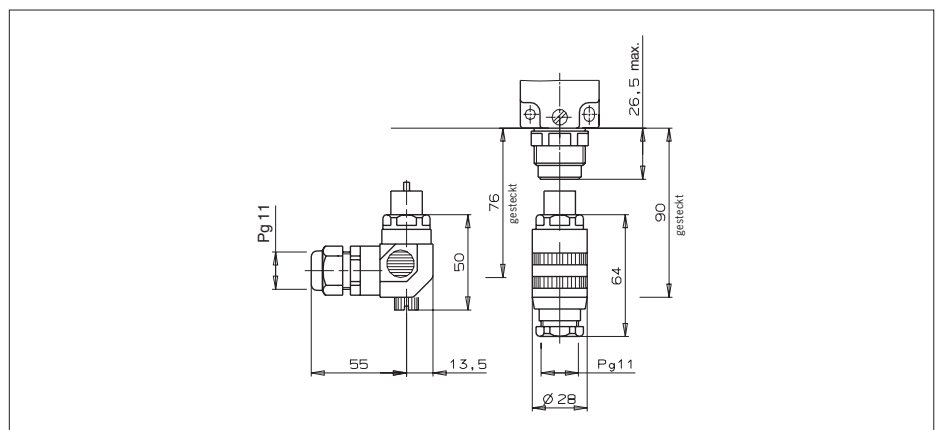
Maßzeichnung NZ2VZ-5... mit Steckerverbinder SR6
